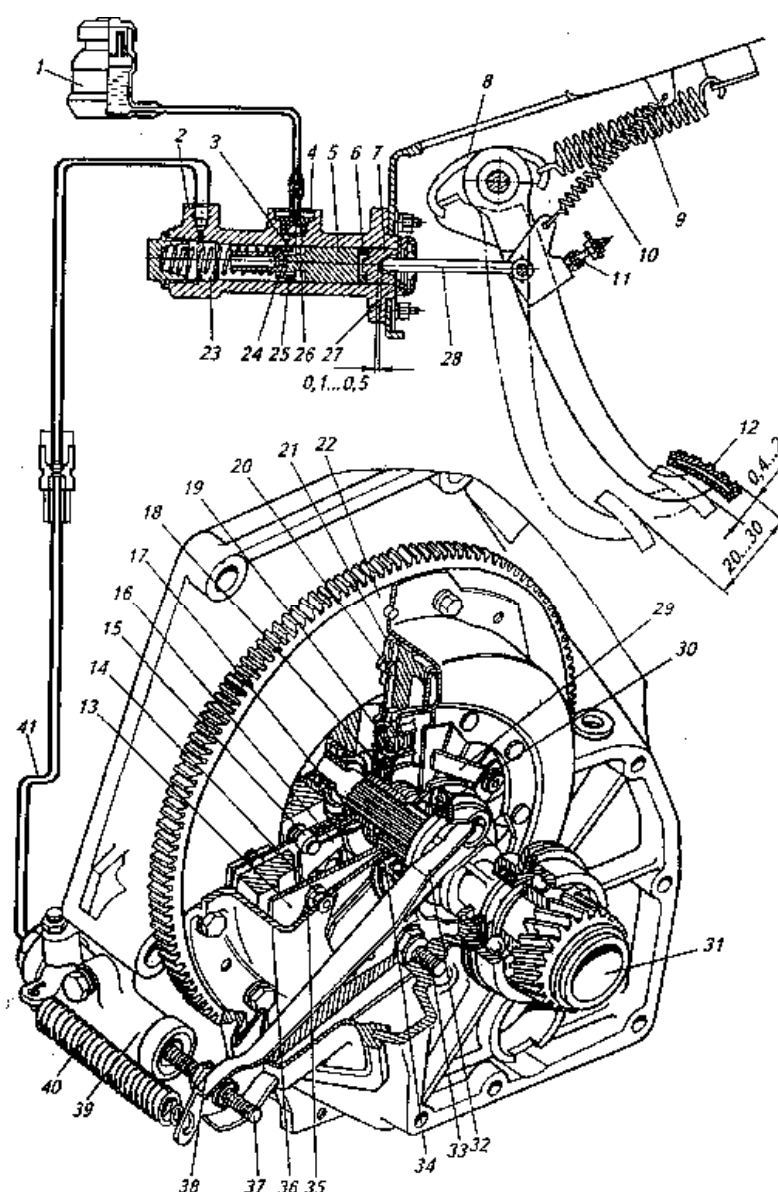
Сцепление и привод сцепления автомобиля ВАЗ-21213: 1 — бачок для тормозной жидкости; 2 — главный гидроцилиндр; 3 — компенсационное отверстие; 4 — штуцер; 5, 7 — поршни; 6, 25 —
